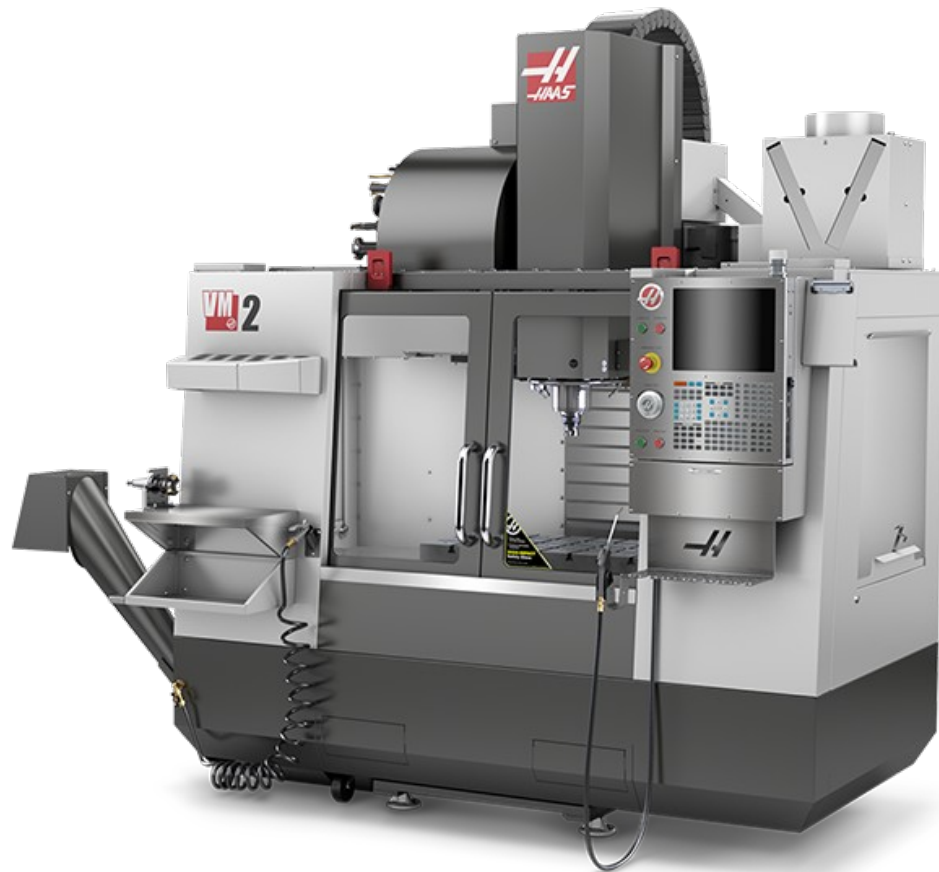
вертикально фрезерний верстат HAAS VM-2
